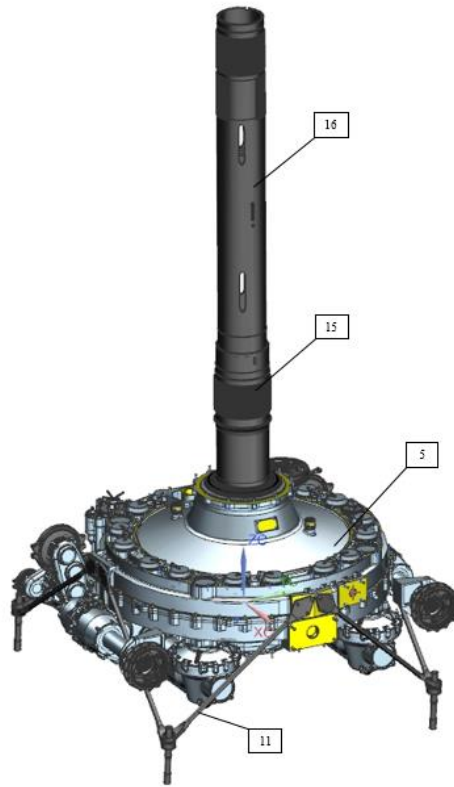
Главный редуктор ВР-450, вид сбоку
